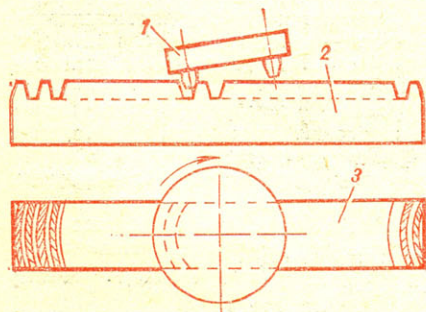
Схема нарезания рейки с КЛЗ: 1 — режцовая головка; 2, 3 — рейка.
